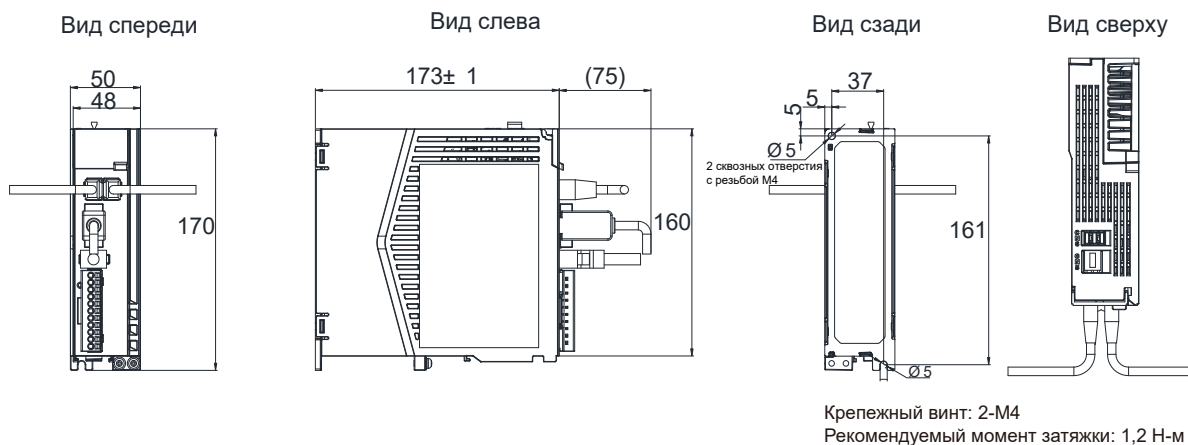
Габаритные размеры для типоразмера А (ед. изм: мм)
